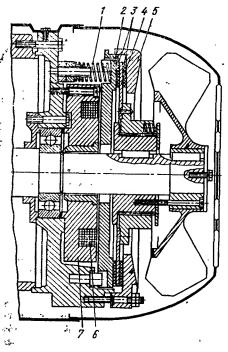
Тормозное устройство двигателя 4A160E.
